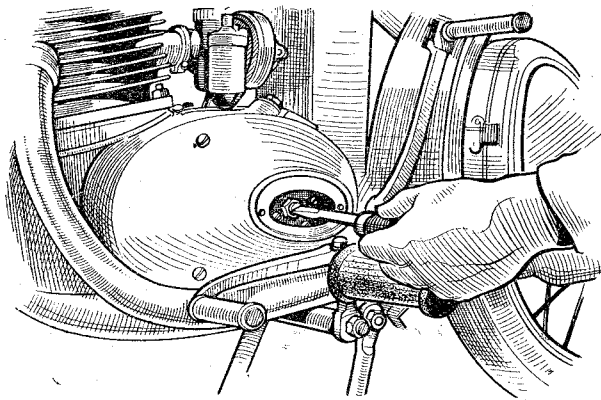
RÉGLAGE DES RESSORTS D'EMBRAYAGE
